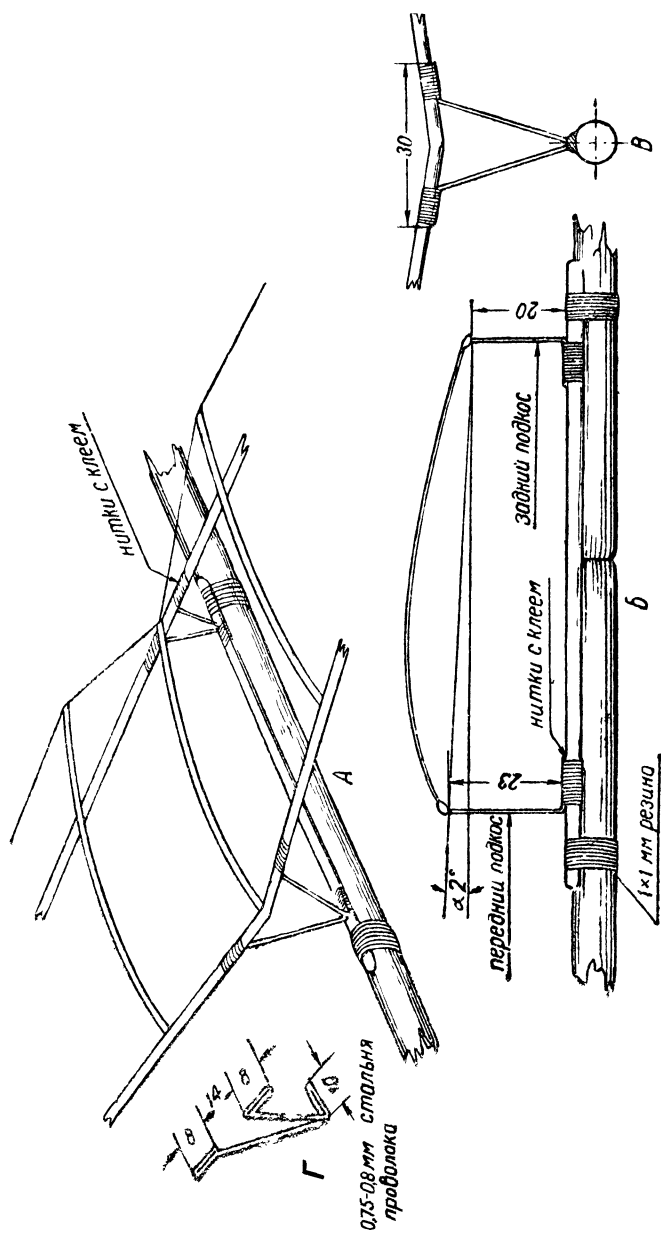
Крепление крыла. А—общий вид крепления; Б—вид крепления сбоку; В—вид крепления спереди; Г—общий вид подкоса для крепления крыла
